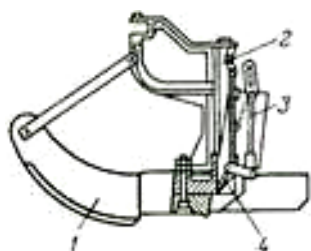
Вид ползоровидного сошника с клапаном
